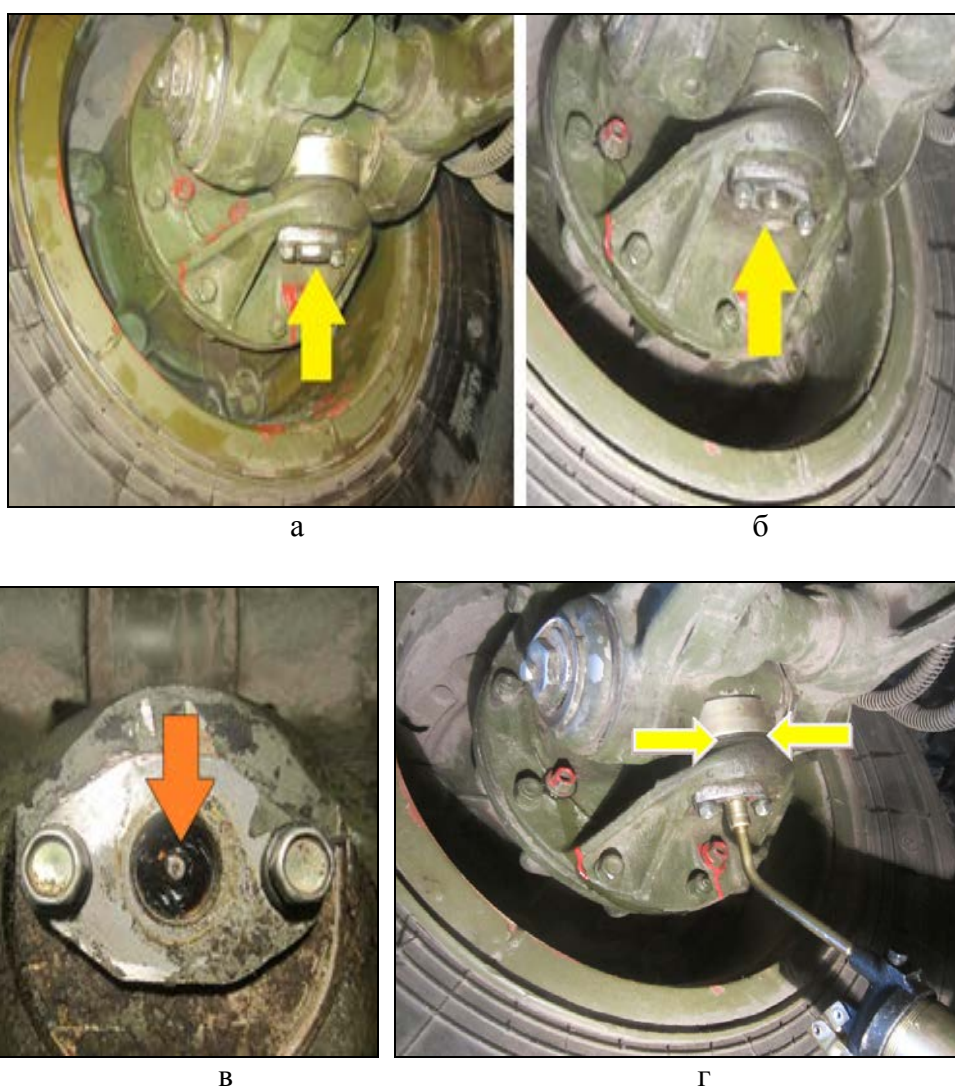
ОК-16 – Подвеска управляемых колес БТР-80
